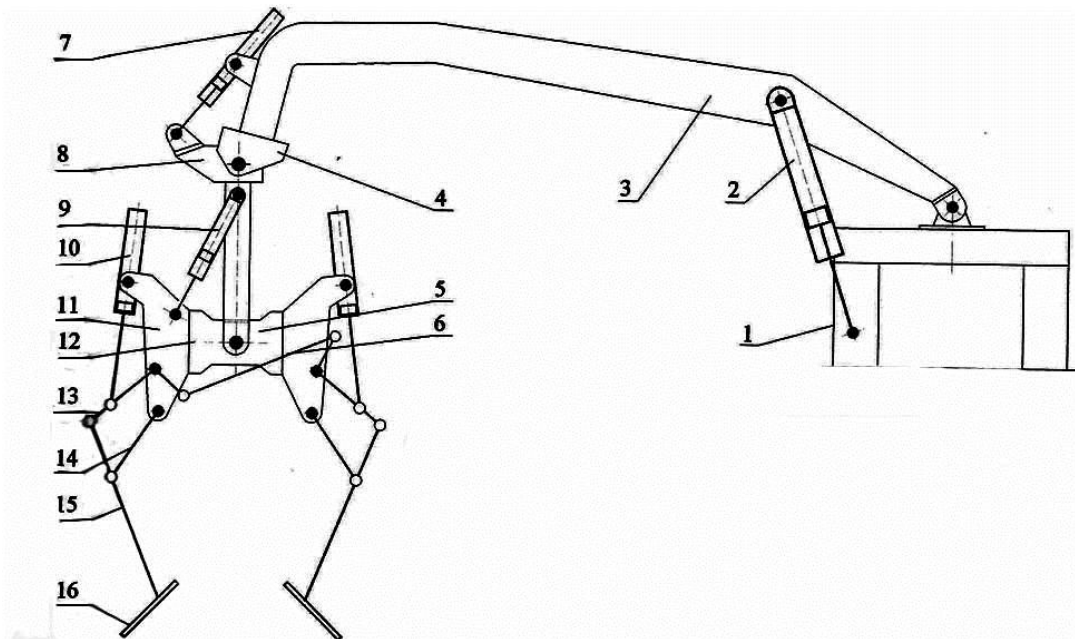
Схема устаткування для ущільнення ґрунту: 1 – портал; 2 – гідроциліндри стріли; 3 – стріла; 4 – механізм розв’язки; 5 – траверса; 6 – штанга; 7 – гідроциліндр підвісу; 8 – підвіс; 9 – гідроциліндр траверси; 10 – гідроциліндр приводу механізму; 11 – боковина; 12 – вставка; 13 – важіль привідний; 14 – важіль нижній; 15 – лапа; 16 – ущільнювальна поверхня.
